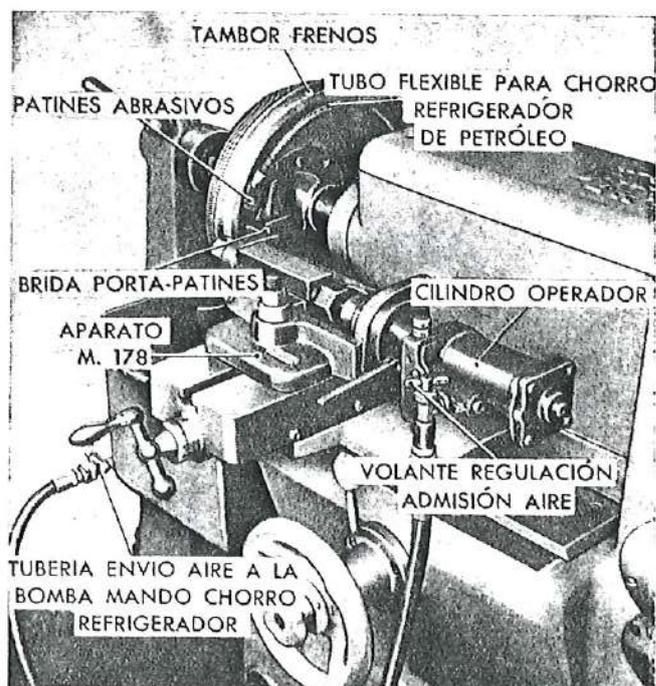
Alisado de un tambor de frenos mediante el aparato M. 178 montado sobre el torno M. 10.
